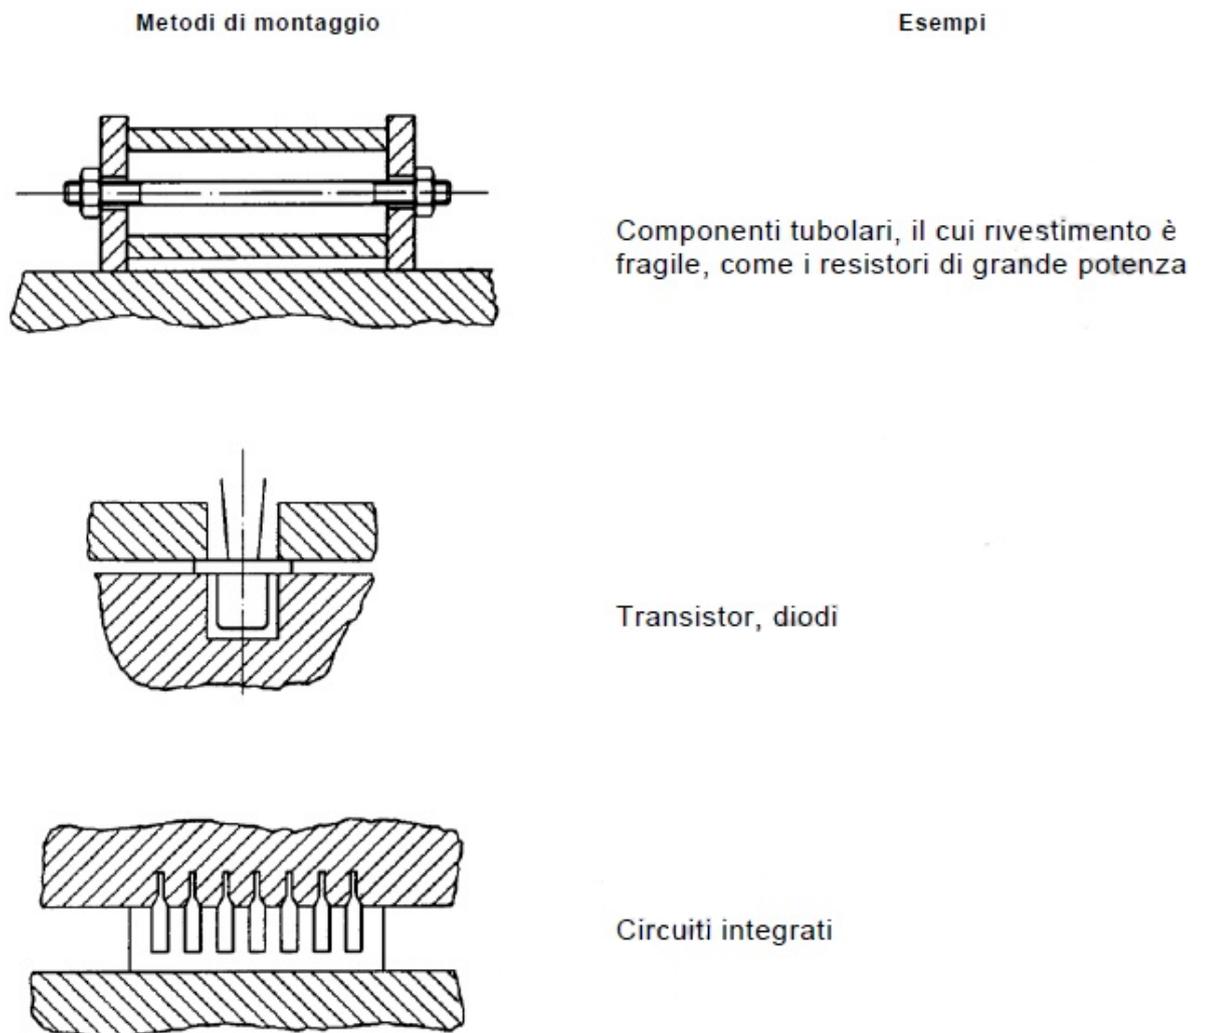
Esempi di montaggio di componenti solo mediante il corpo
